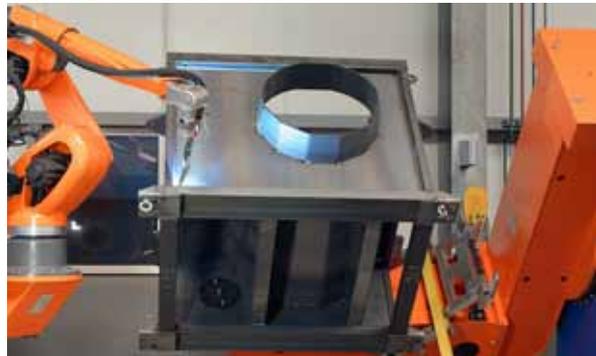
Der 1,5-Tonnen-Werkstückpositionierer bringt die Maschinengehäuse immer in eine für das Schweißen optimale Position.
